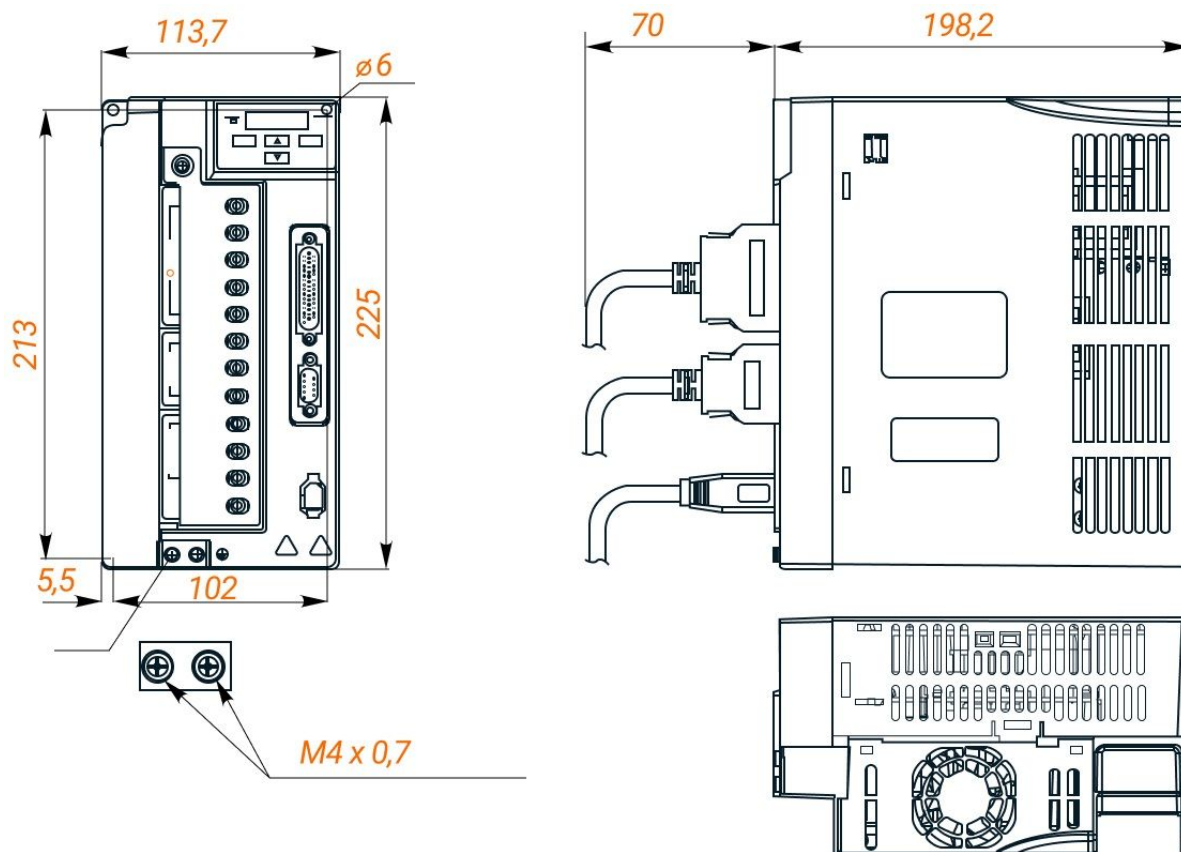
Габаритные размеры и схематичный вид серводрайвера K3N
